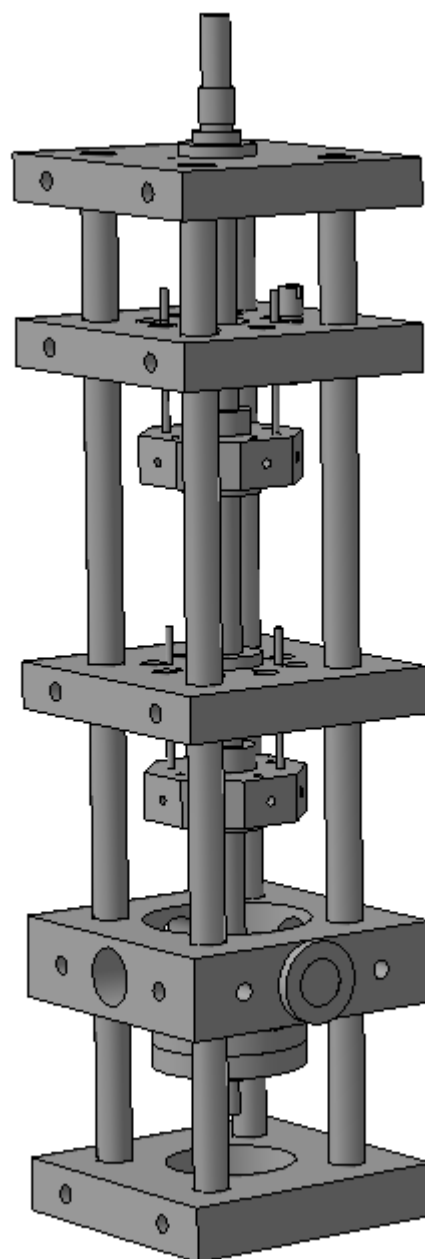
Имитационный стенд для исследования металлообрабатывающего оборудования. 3Dмодель.
